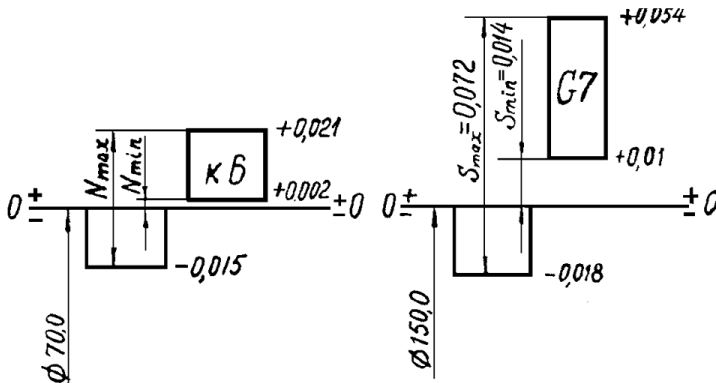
Схемы полей допусков соединений: внутреннее кольцо-вал и наружное кольцо-корпус
